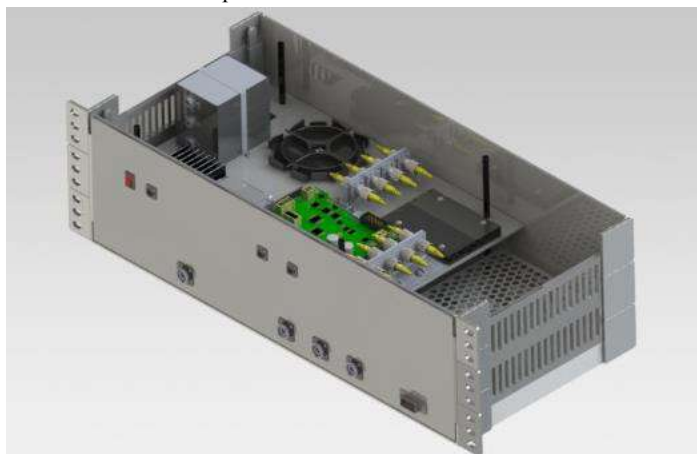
Установка для измерения хроматической дисперсии без крышки: вид в изометрии
